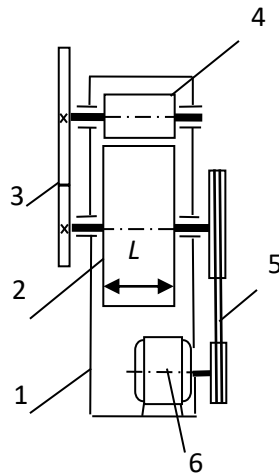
Кінематична схема приведення в дію верстата: 1 – корпус; 3 – зубчаста передача; 2 – робочий валок; 5 – клинопасова передача; 4 – живильний валок; 6 – електродвигун
